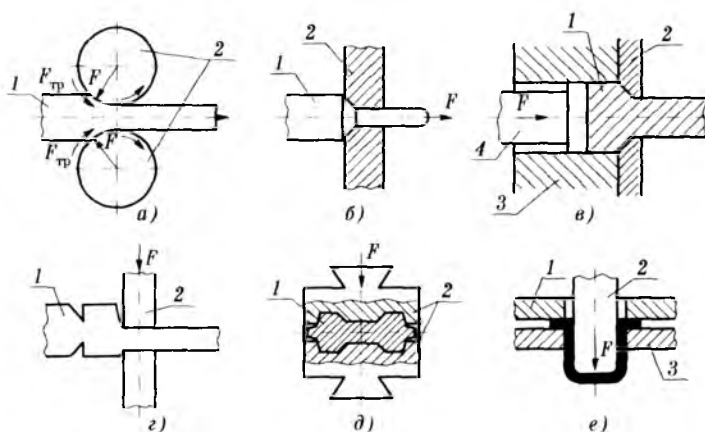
Схемы основных способов обработки металлов давлением:
